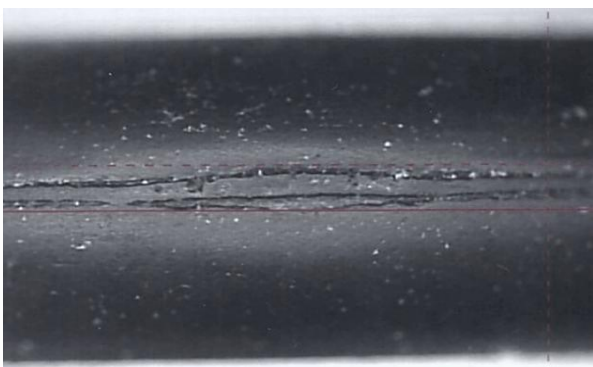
Schrumpfriss auf einem O-Ring in der Draufsicht bei 40-facher Vergrößerung (Bild: OPR Elastolabs)
